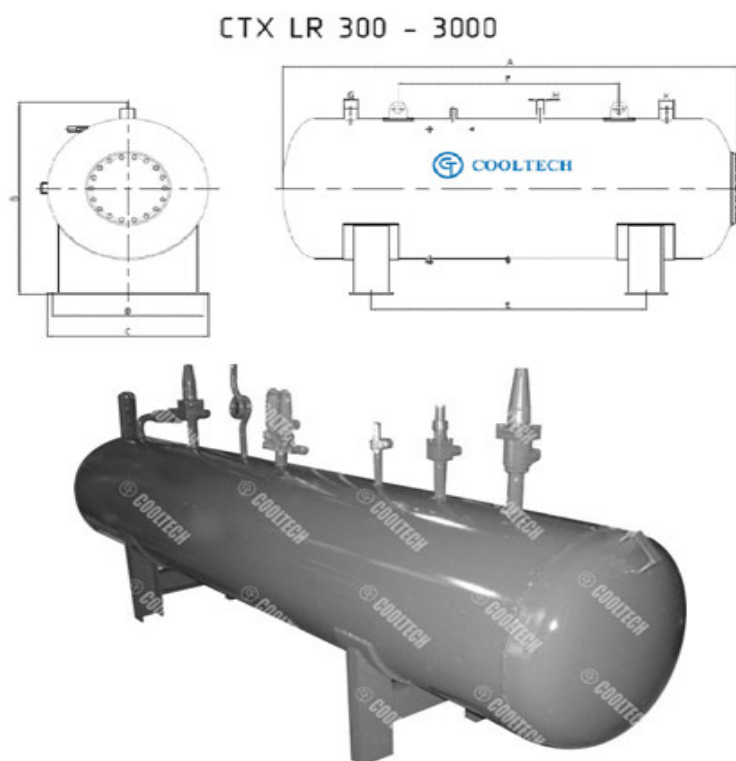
Горизонтальний ресивер COOLTECH CTXLR
